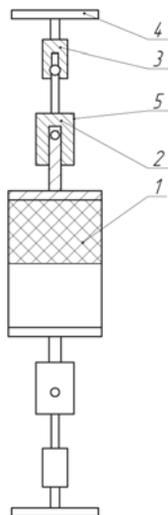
Приспособление для испытаний: 1 – образец; 2, 3, 5 – шарнирное сочленение; 4 – захваты машины
